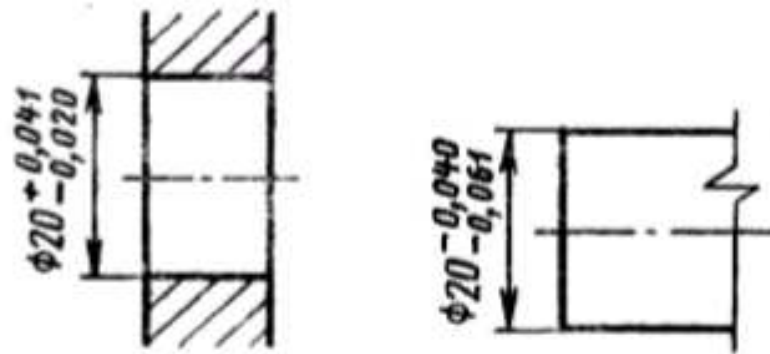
Обозначение допусков на рабочих чертежах
